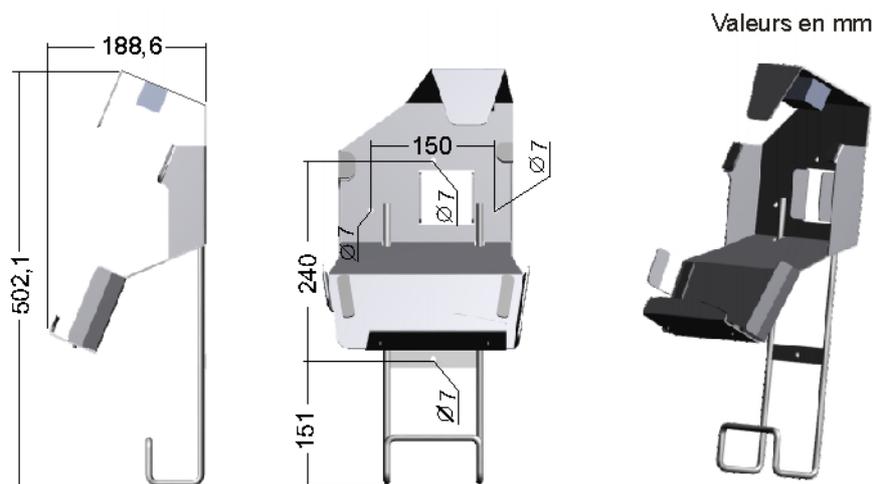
Dimensions et cotes de perçage du support smartPAD
